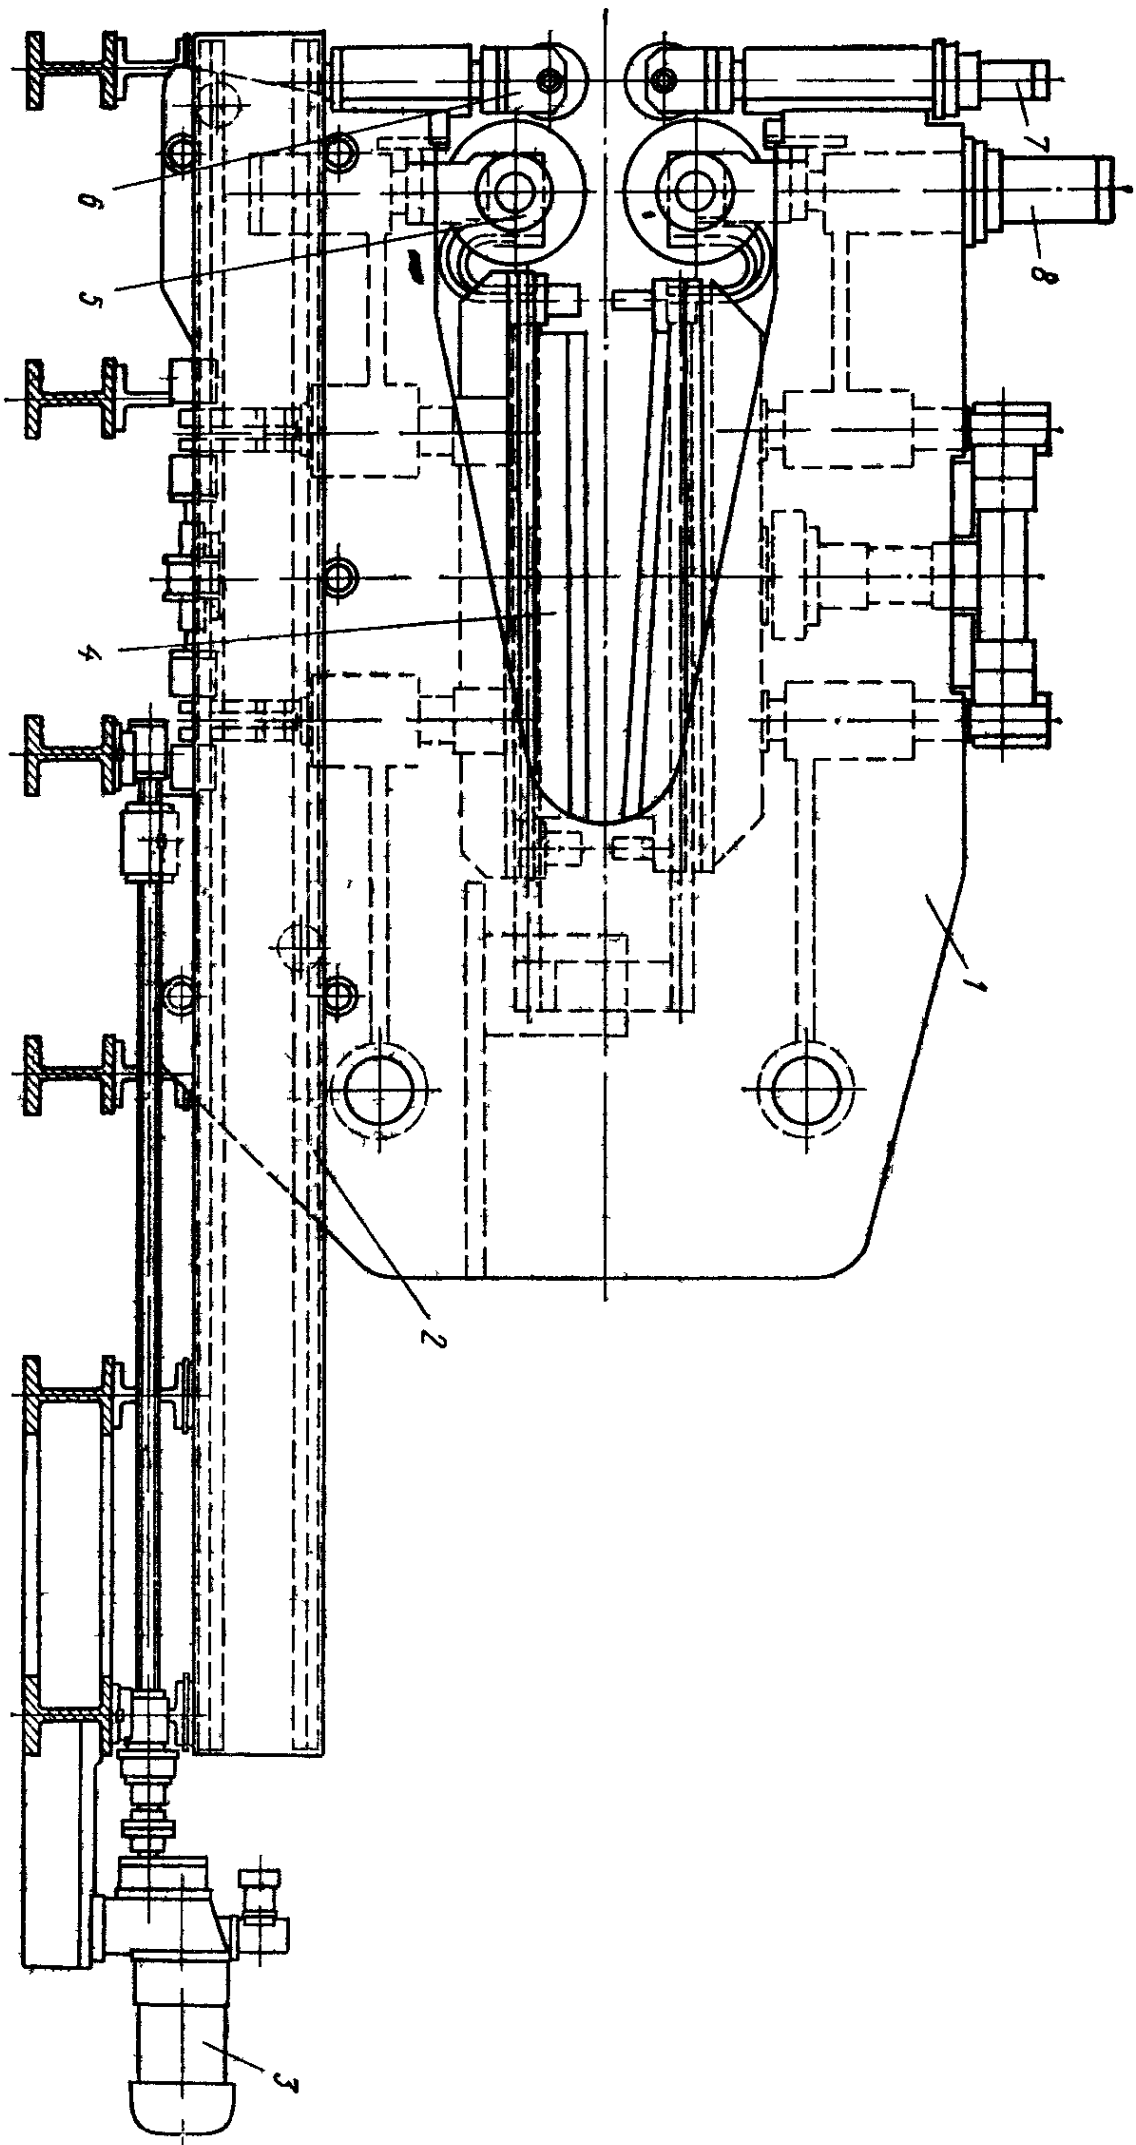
Машина для сварки полос с раздавливанием кромок
